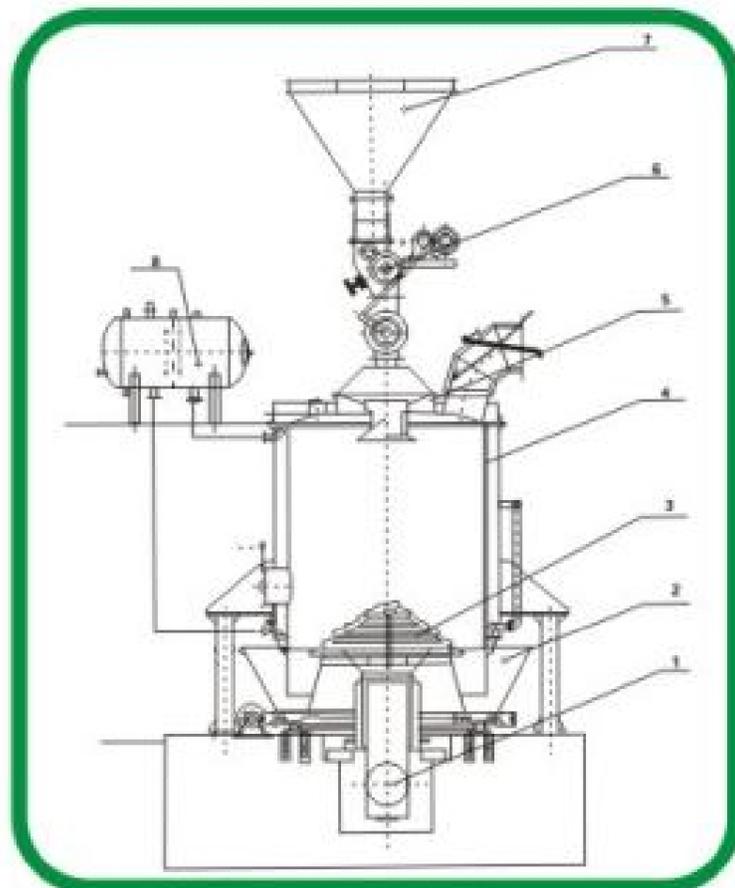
Устройство одностадийного газификатора угля с механической загрузкой
